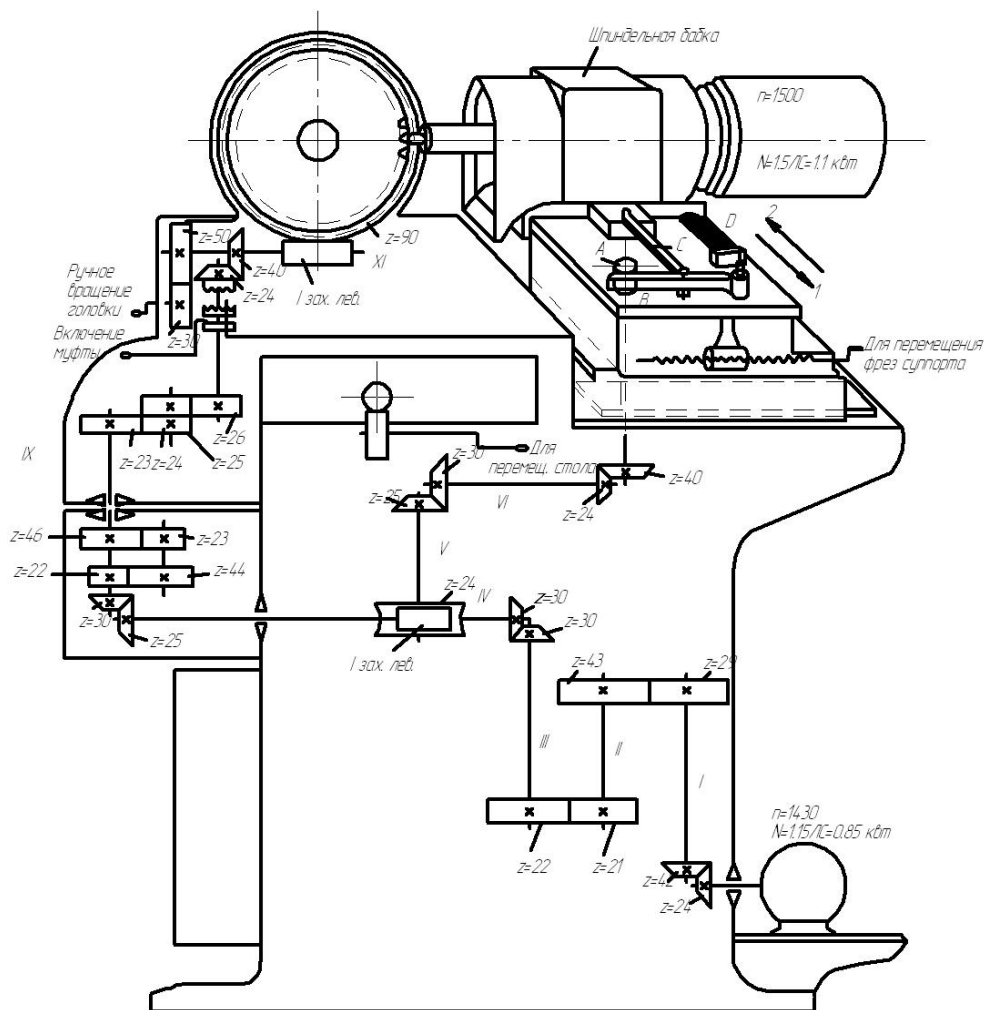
Кинематическая схема зубозакругляющего станка фирмы “Рейнекер ”
